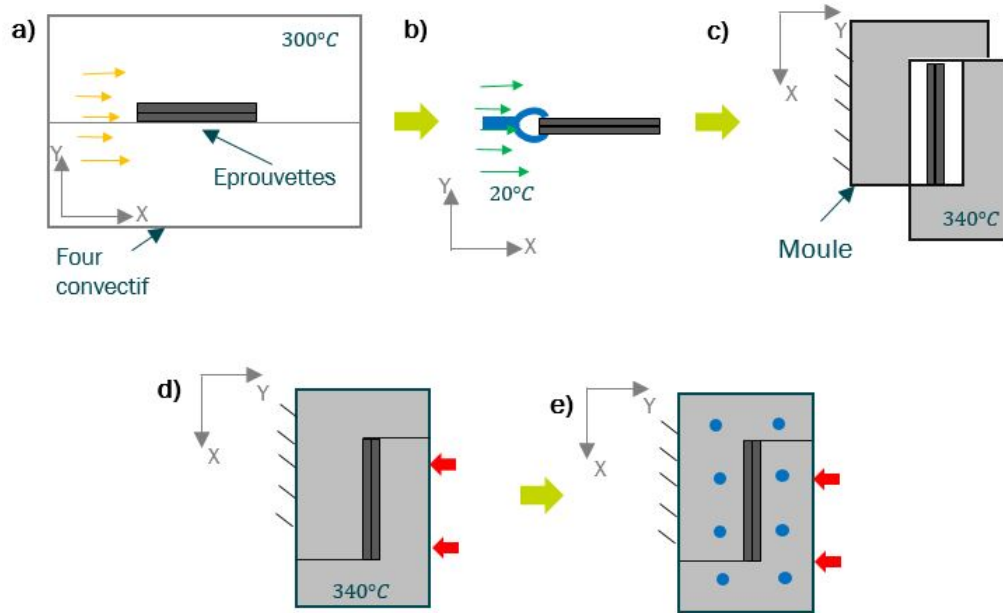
Procédé de soudage des deux éprouvettes : a) Préchauffage, b) Transfert, c) Positionnement, d) Soudage et, e) Refroidissement.
